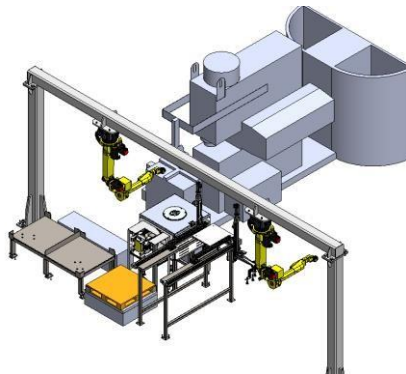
Vista isométrica de parte izquierda de la celda donde se lleva acabo el proceso de maquinado y paletizado de rotor.
